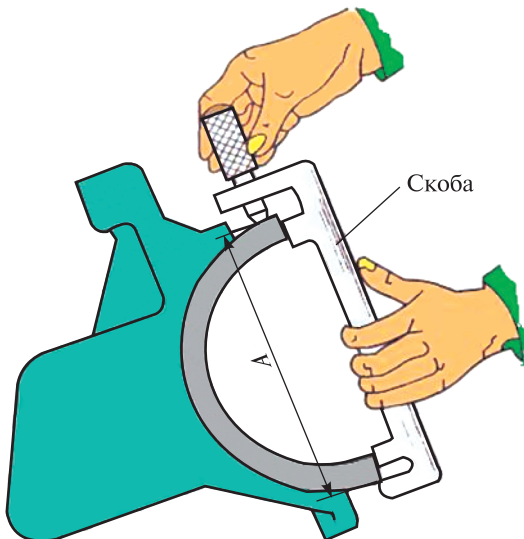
Измерение расстояния между посадочными поверхностями на буксе моторно-осевого подшипника с помощью микрометрической скобы
